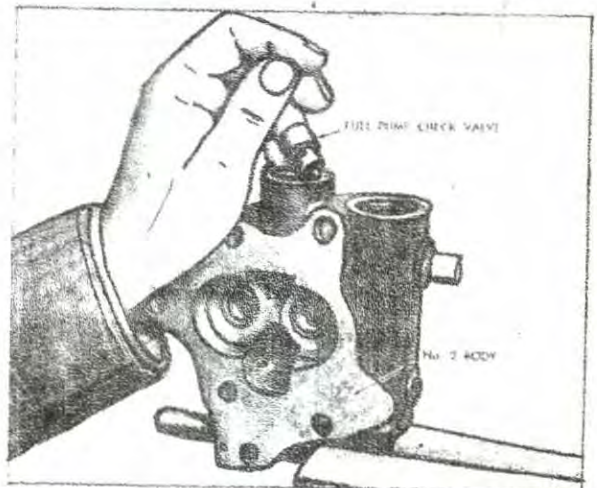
Desmontaje de la válvula de retención del combustible.
